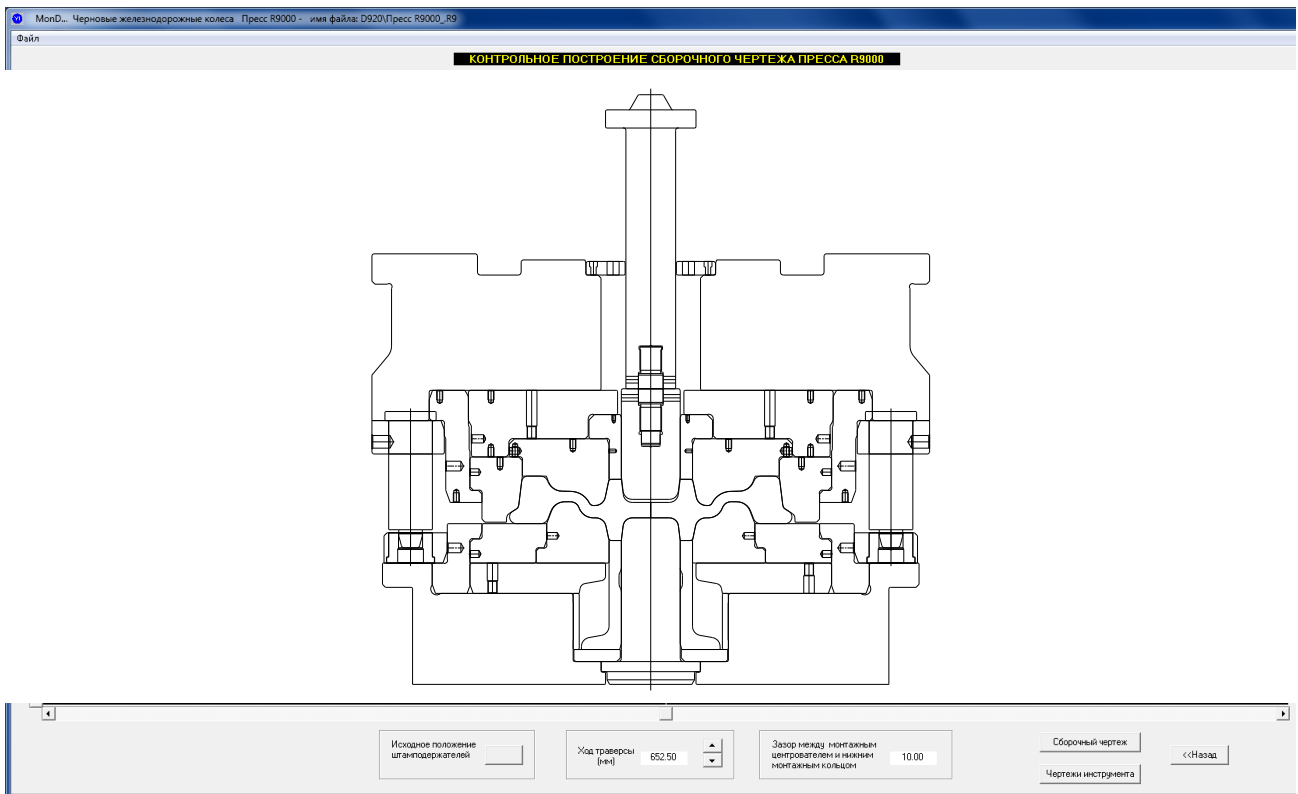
Проектирование сборочного чертежа инструмента деформации формовочного пресса
